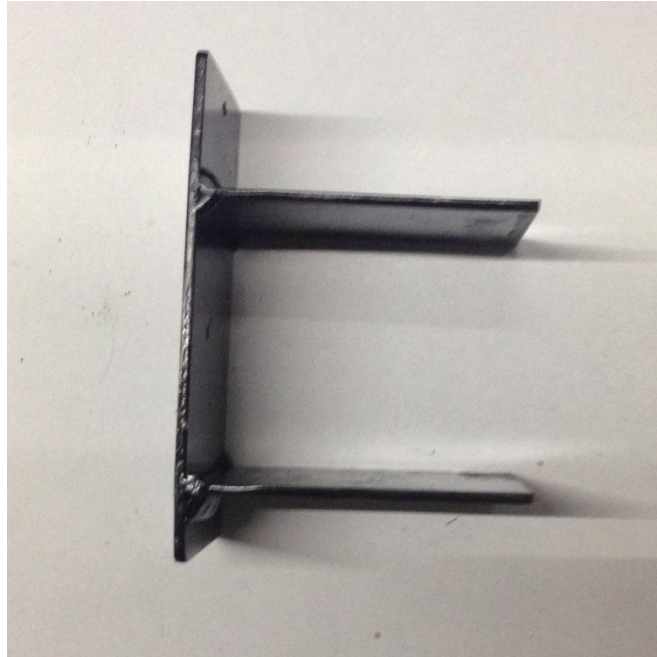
Chapas de ferro laterais, soldadas a base dos motores.
